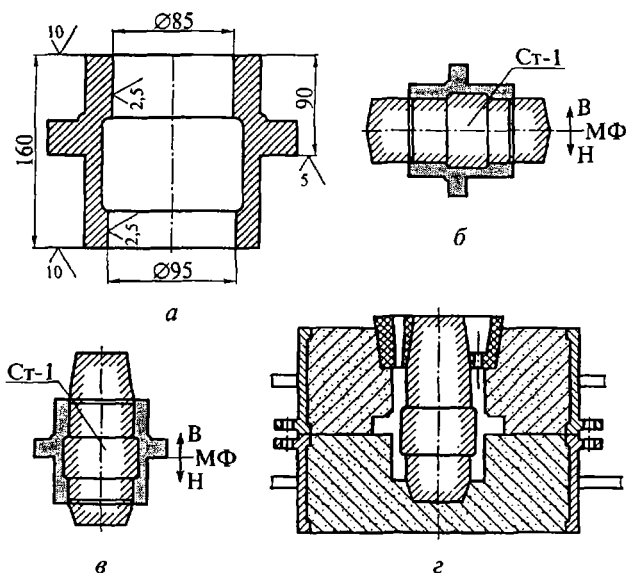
Разработка технологического процесса изготовления отливки корпуса подшипника:
